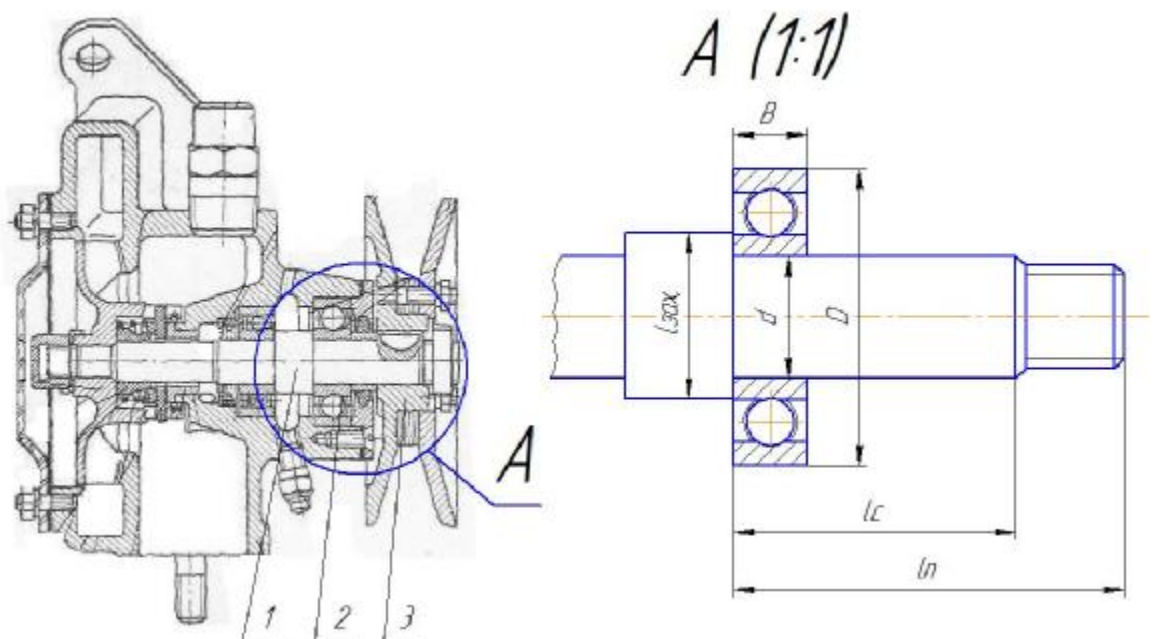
Схема встановлення підшипника на валу насоса системи охолодження автомобіля МАЗ-5335: 1 – вал; 2 – кульковий підшипник; 3 – шків.
